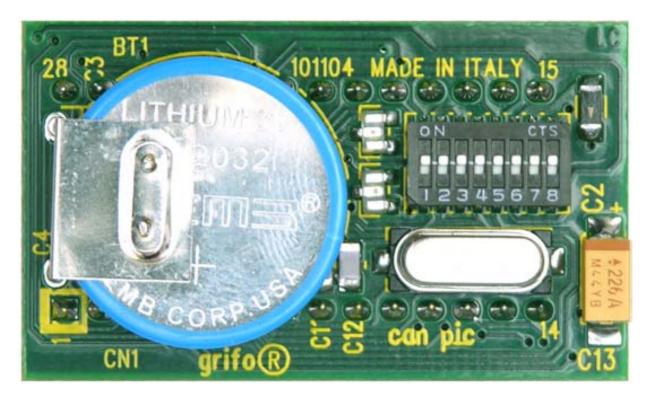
VISTA DALL'ALTO DELLA CAN PIC
